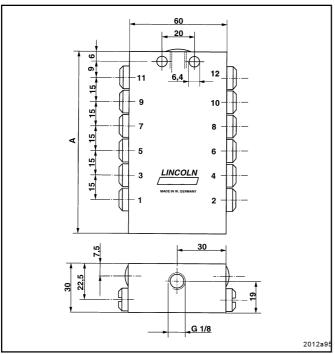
Cotes dimensionnelles du doseur SSV installé en bas
